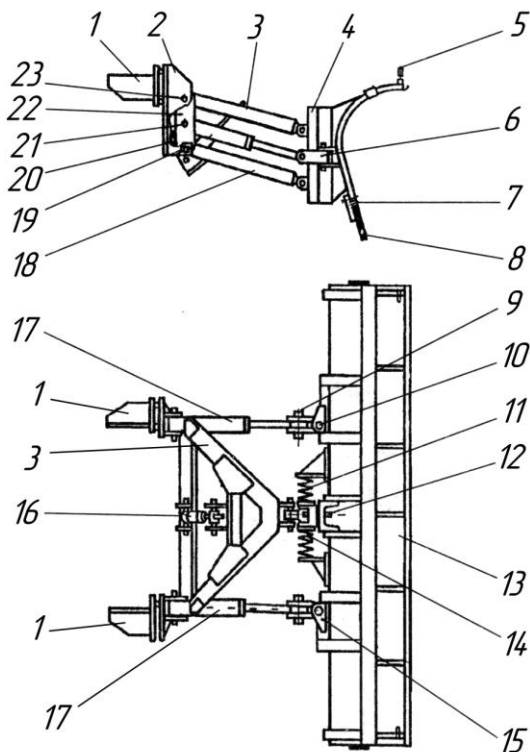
Конструктивная схема поворотного отвала:
